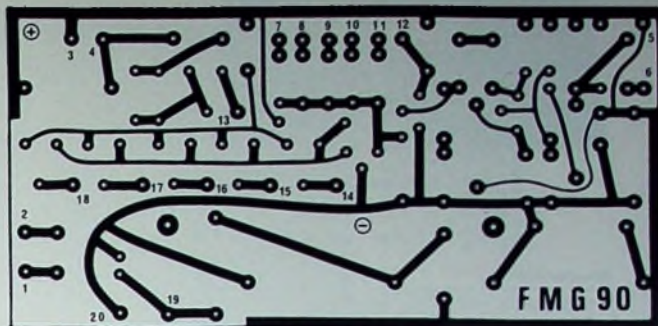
Printplatte für den Frequenzmesser (Maßstab 1 : 2)
